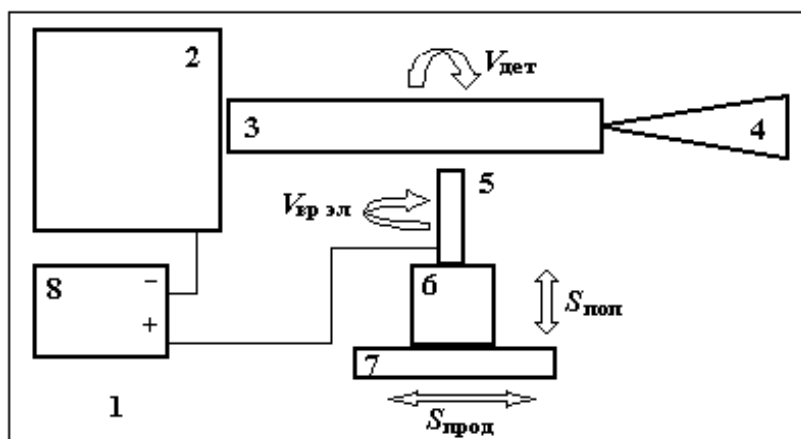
Схема установки механизированного ЭИЛ IMES-1001: 1 – база токарного станка; 2 – изолированный кулачковый патрон; 3 – легируемая деталь; 4 – изолированная задняя бабка; 5 – торцевой вращающийся электрод; 6 – механизированная головка с суппортом станка; 7 – следящая система; 8 – генератор импульсов; $V_{вр.эл}$ – скорость вращения электрода; $V_{дет}$ – скорость вращения детали; $S_{поп}$ – поперечная подача; $S_{прод}$ – продольная подача
